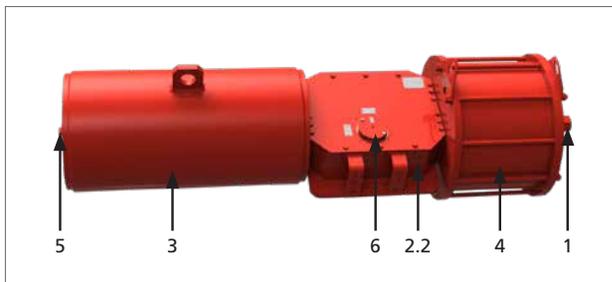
Componentes principais do GPIS (corpo soldado)
